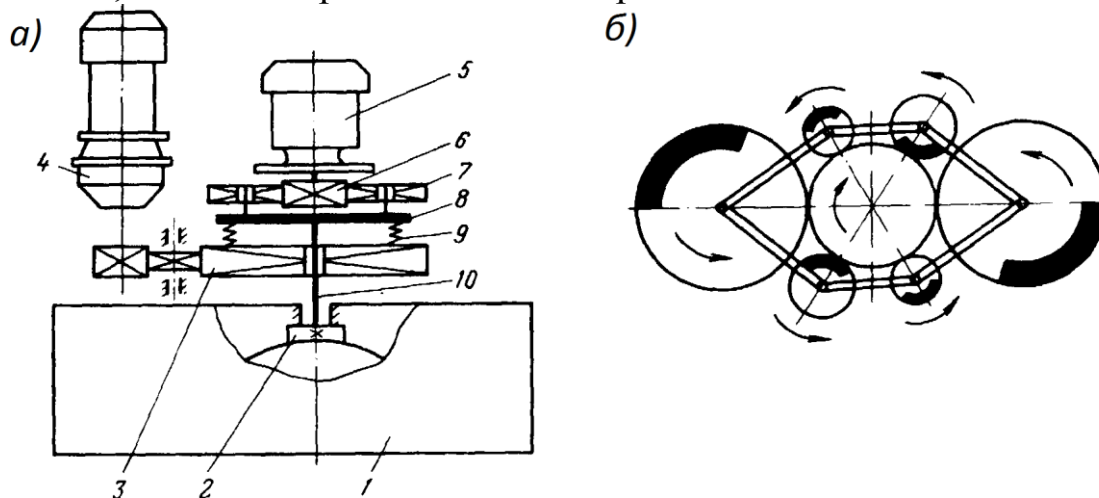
Бетоносмеситель с активными рабочими органами: а – кинематическая схема; б – расположение сателлитов; 1 – корпус; 2 – лопастной механизм; 3 – ведомое колесо; 4 – мотор-редуктор; 5 – привод вибратора; 6 – центральное колесо; 7 – сателлиты; 8 – водило; 9 – пружины; 10 – шпиндель
